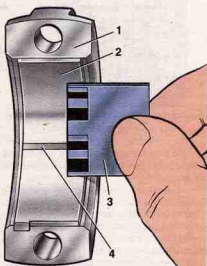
Измерение зазора в шатунном подшипнике: 1 – сплюсненная калиброванная пластмассовая проволока; 2 – вкладыш; 3 – шкала шатуна; 4 – шкала для измерения зазора
